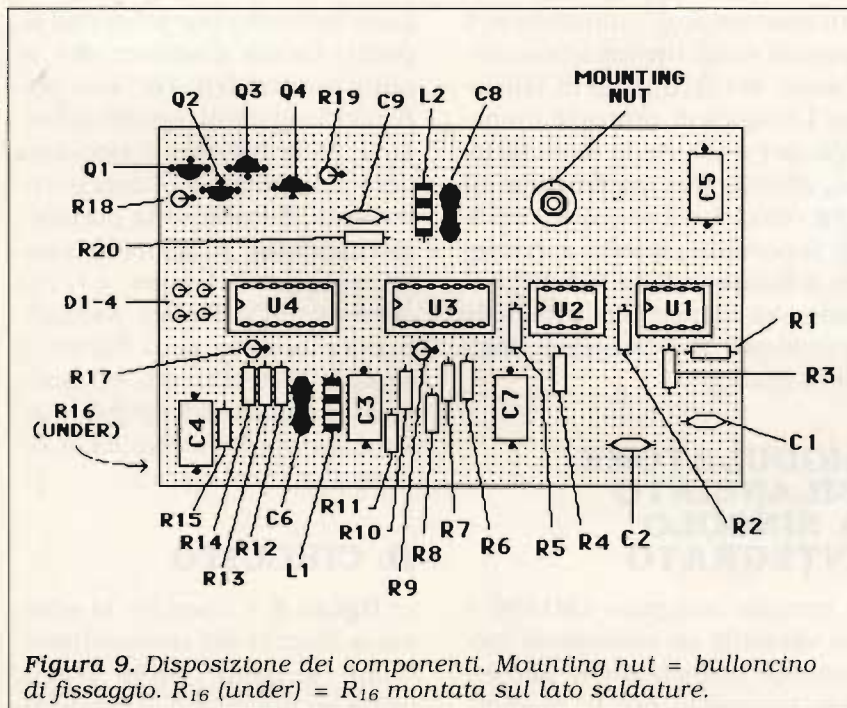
Disposizione dei componenti. Mounting nut = bulloncino di fissaggio. R16 (under) = R16 montata sul lato saldature.
